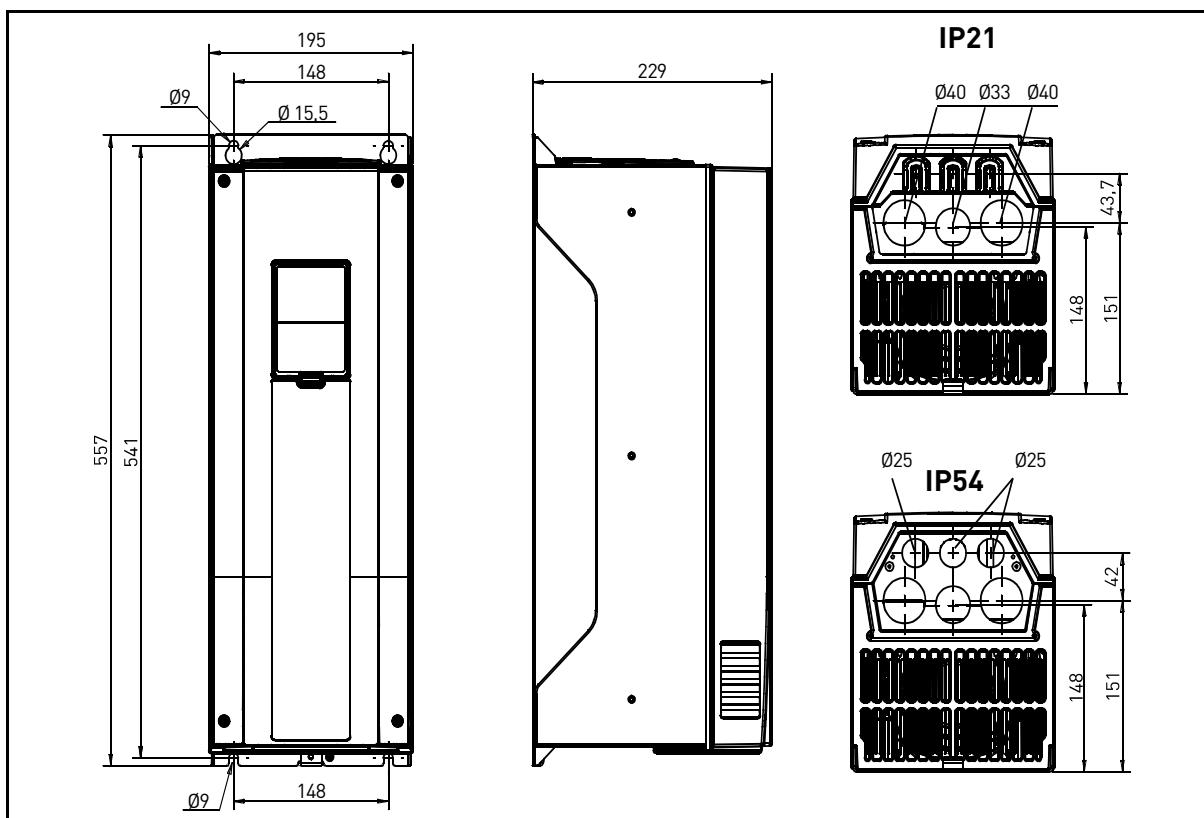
Dimensões do inversor de CA Vacon, MR6, montagem na parede
